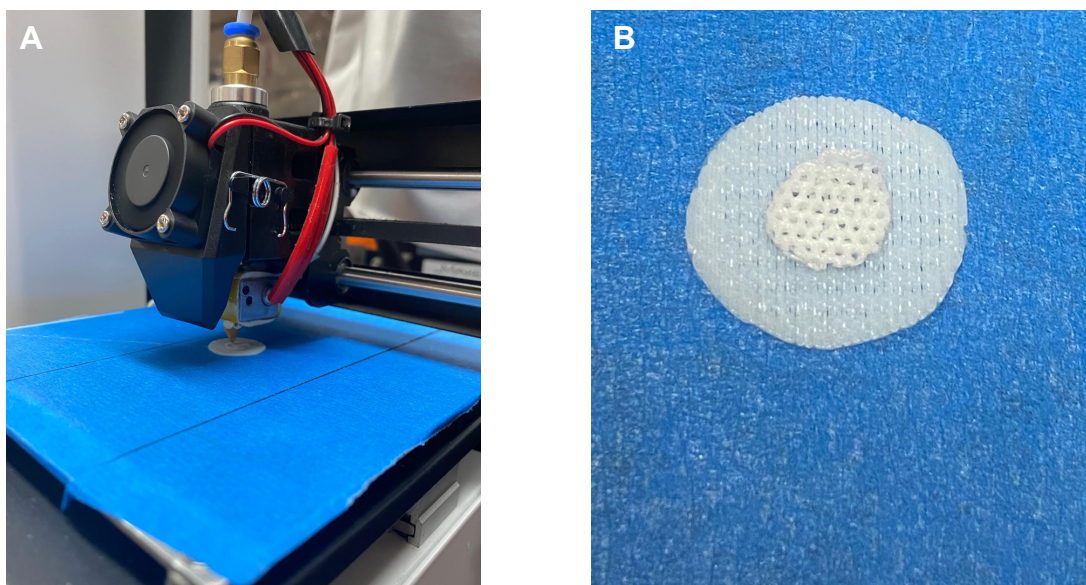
A) Impresión de andamios con impresora Monoprice Select - Mini impresora 3D con técnica de deposición fundida capa por capa. B) Andamio impreso finalizado con material de soporte.
